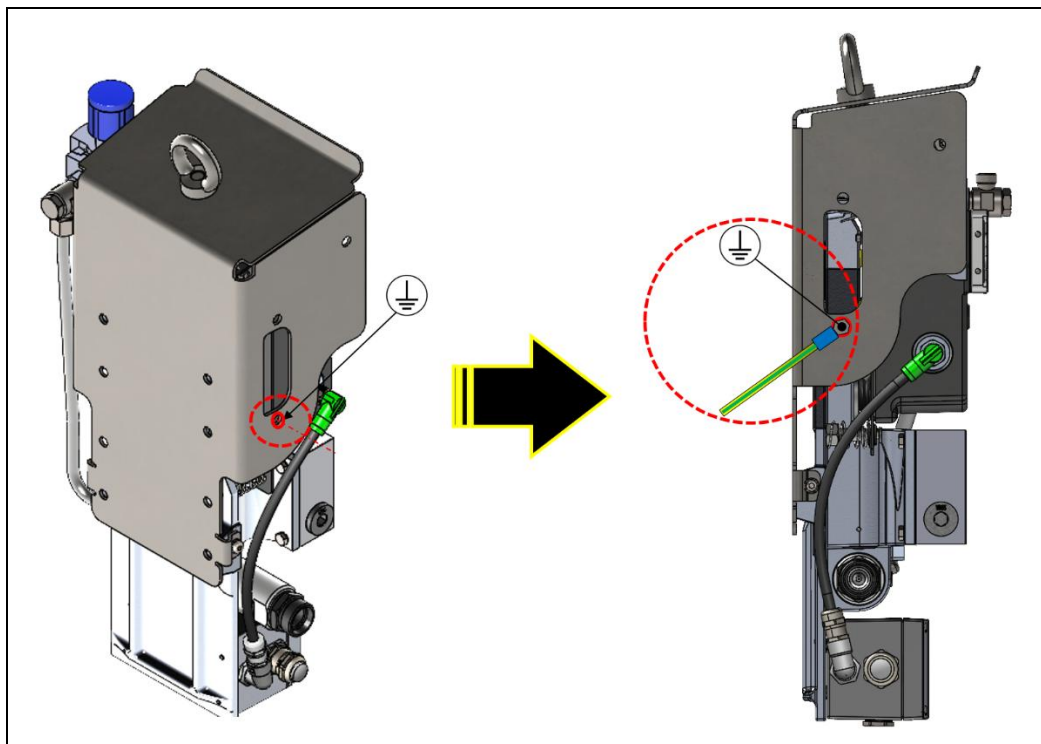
Posizione e installazione, collegamento di messa a terra, calotta di protezione VN2020
